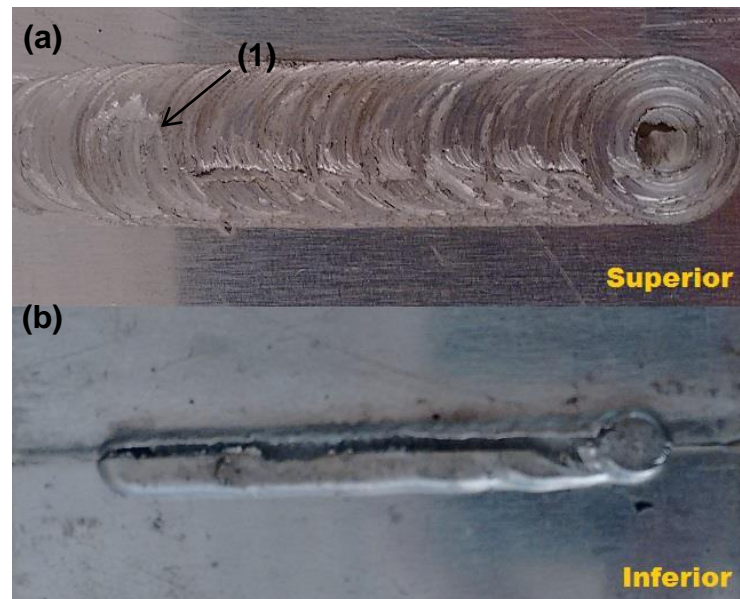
Ensaio de solda com rotação de 1200 RPM e avanço de 60 mm/min. Vistas (a) superior e (b) inferior da solda.
